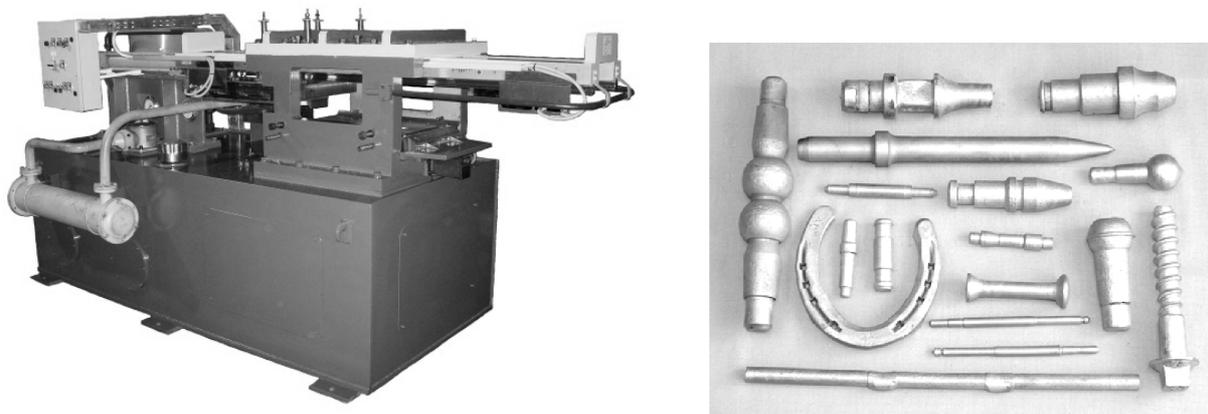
Стан поперечно-клиновой прокатки и прокатанные поковки
